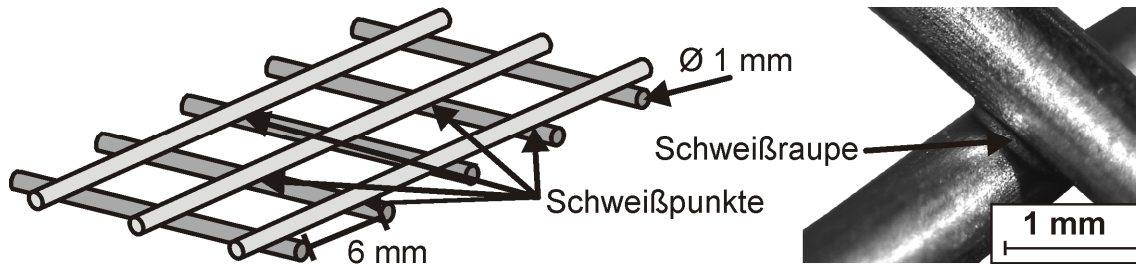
Schema Schweißgitter (links) Aufnahme Schweißpunkt (rechts)
